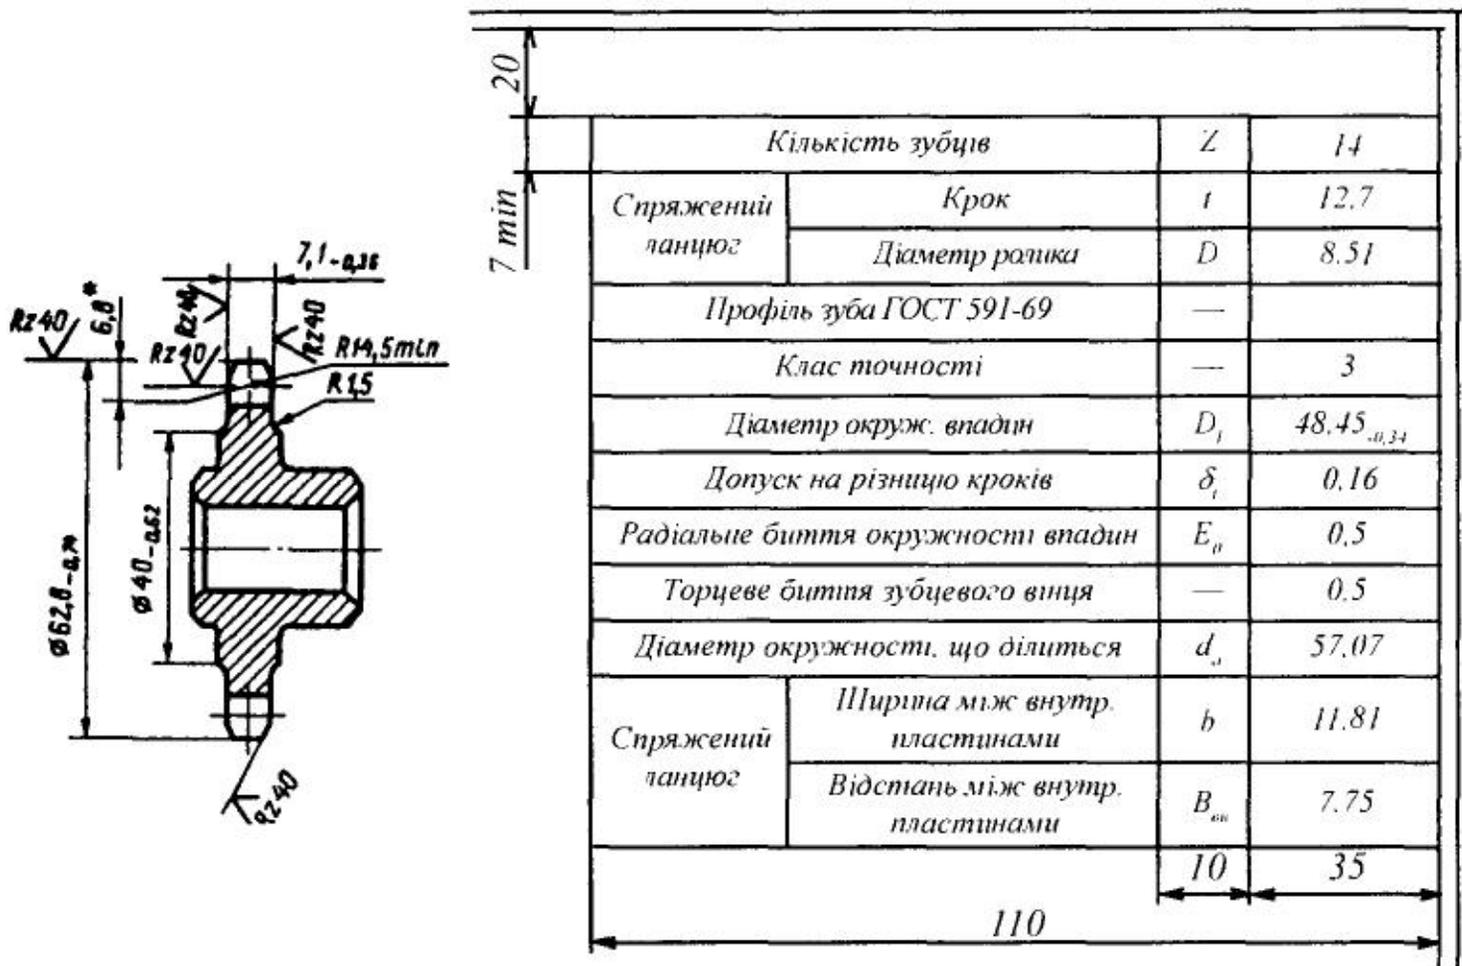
Креслення зірочки ланцюгової передачі.
